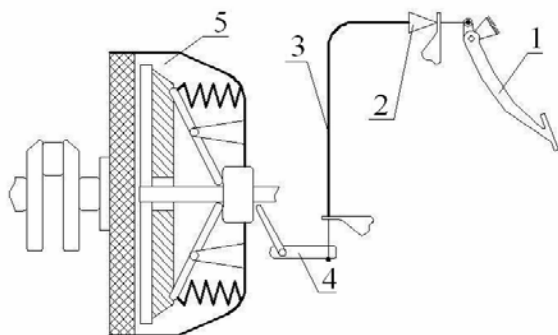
Схема механического тросового привода сцепления: 1 – педаль; 2 – механизм автоматической регулировки длины троса; 3 – трос; 4 – вилка выключения сцепления; 5 – сцепление
